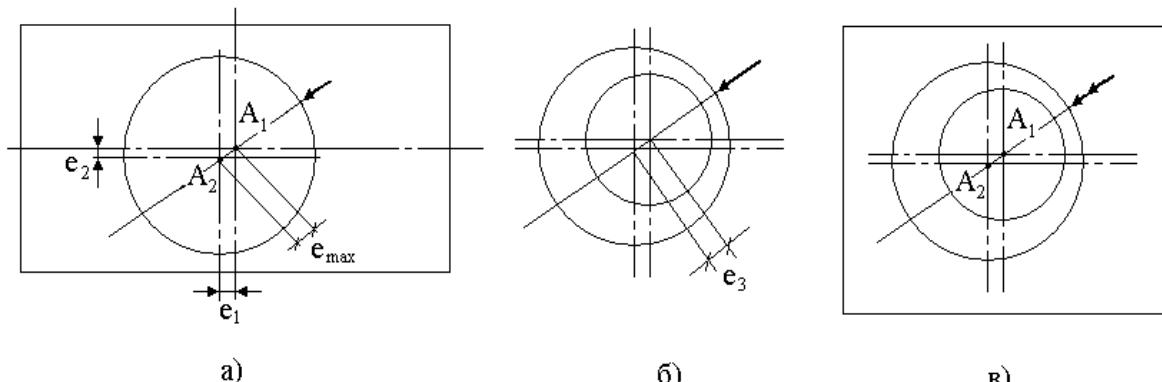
Совмещение оси вращения вала и оси посадочного места корпуса
